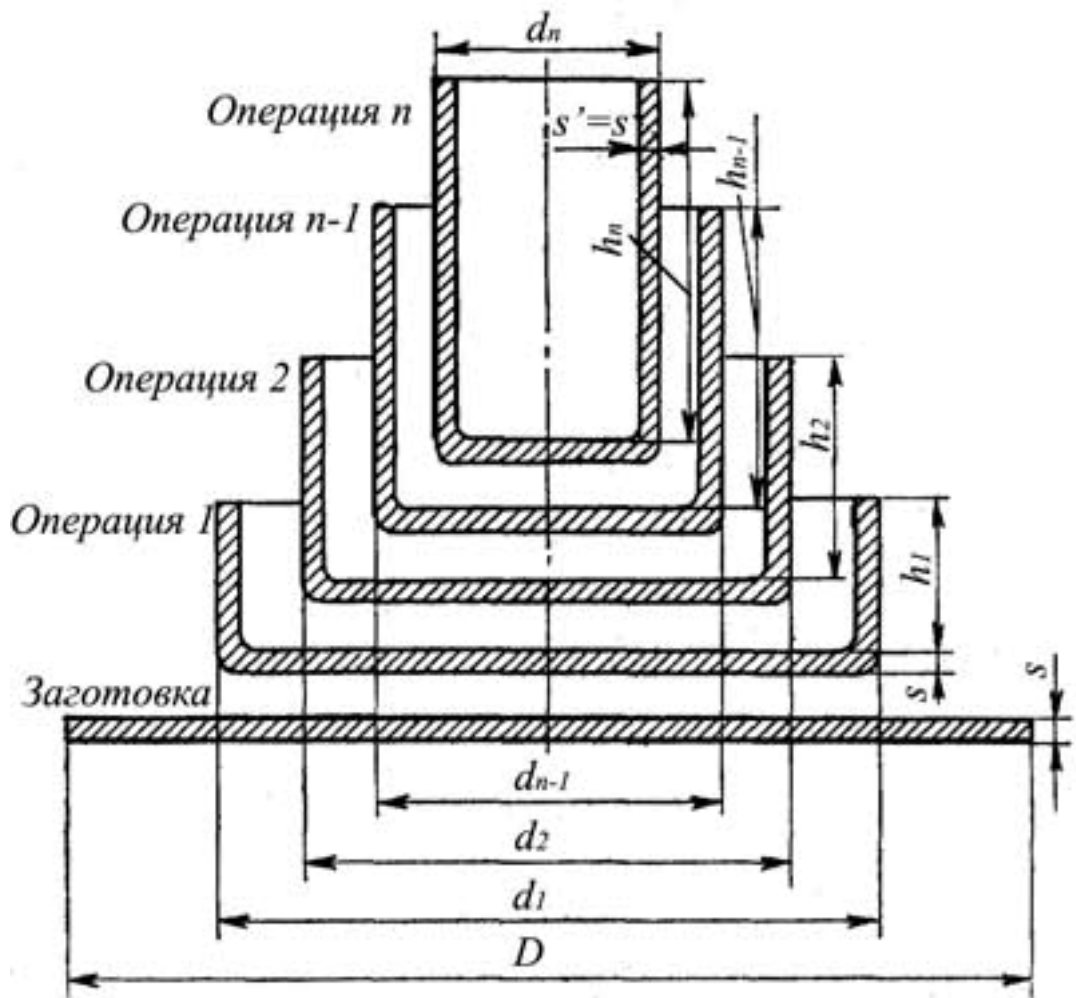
Схема получения полого изделия диаметром d_n и высотой h_n из плоской заготовки диаметром D
